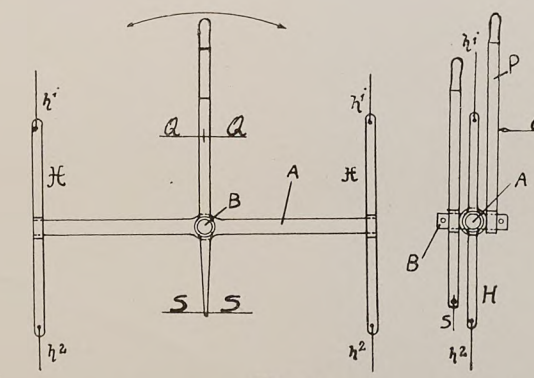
Steuerhebel von August Euler. *A* Achse mit den Hebeln *H* zur Betätigung des Höhensteuers mittels der Seile h^1, h^2 . *B* Achse für die seitliche Schwingung der Steuerhebel *P* für die Quersteuerung mittels Seilen *Q*, *S* für das Seitensteuer.
